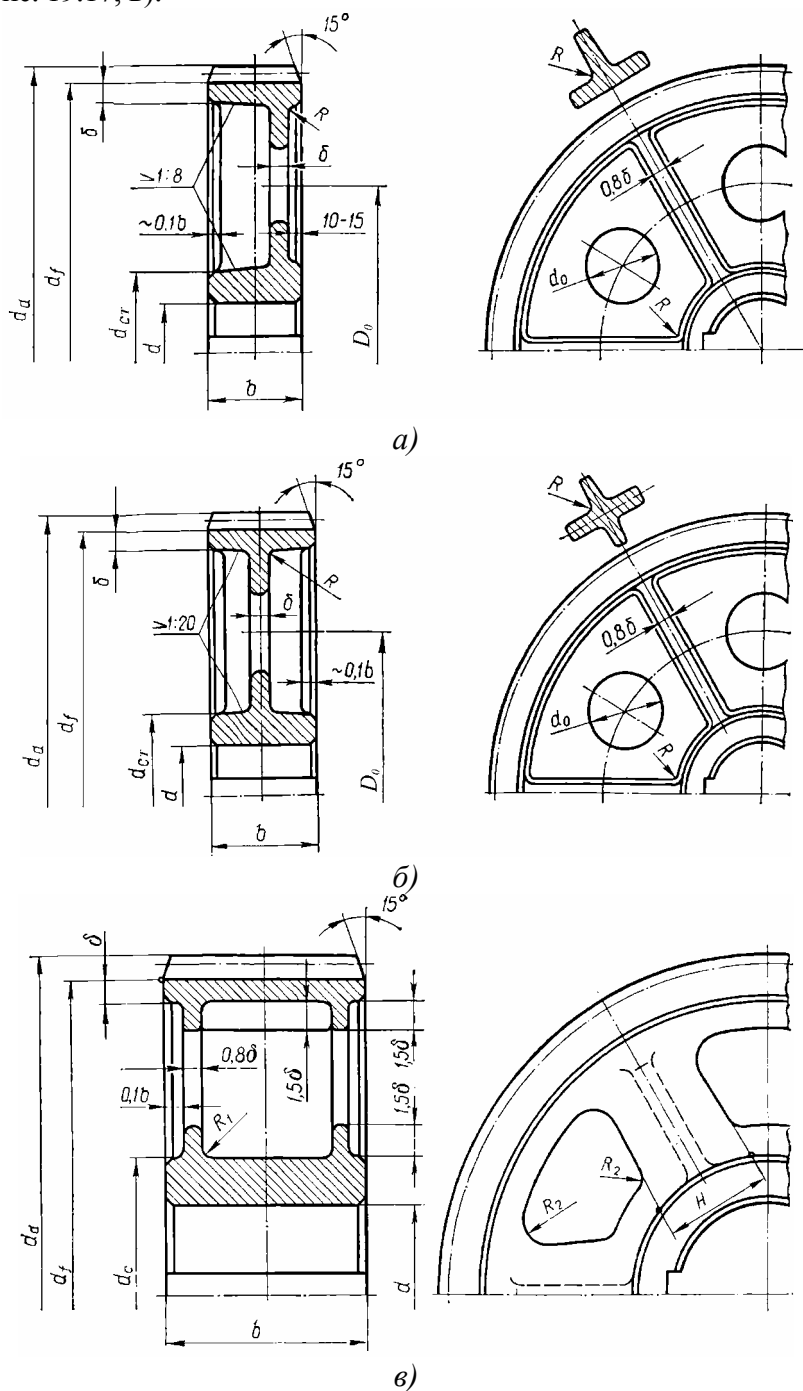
Конструкции литых цилиндрических зубчатых колес
